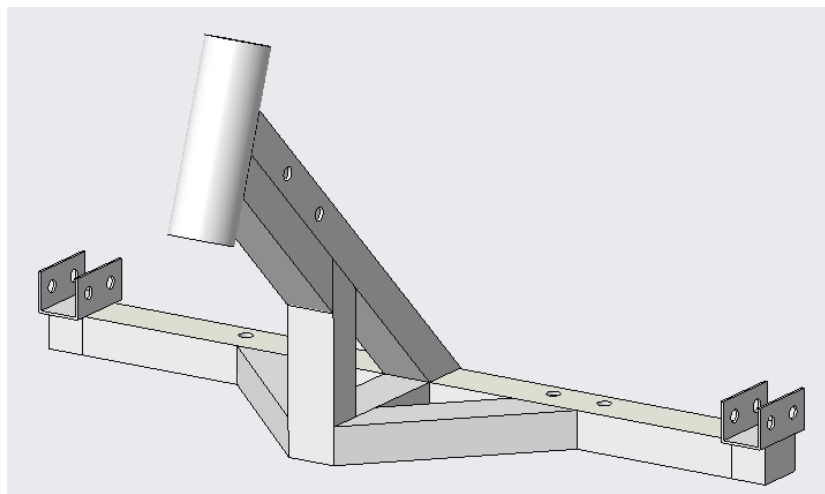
Nosná část rámu krokového motoru s převodovkou
